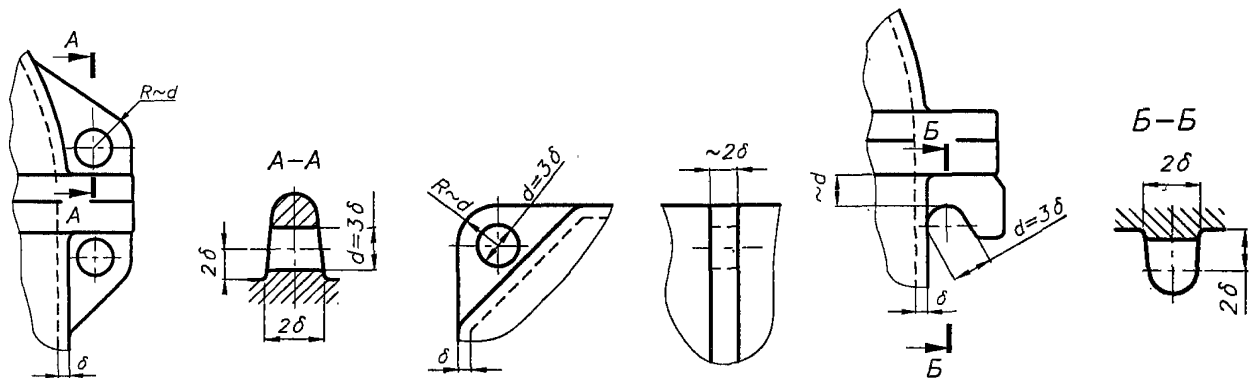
Стрповочные элементы редукторов (проушины)
